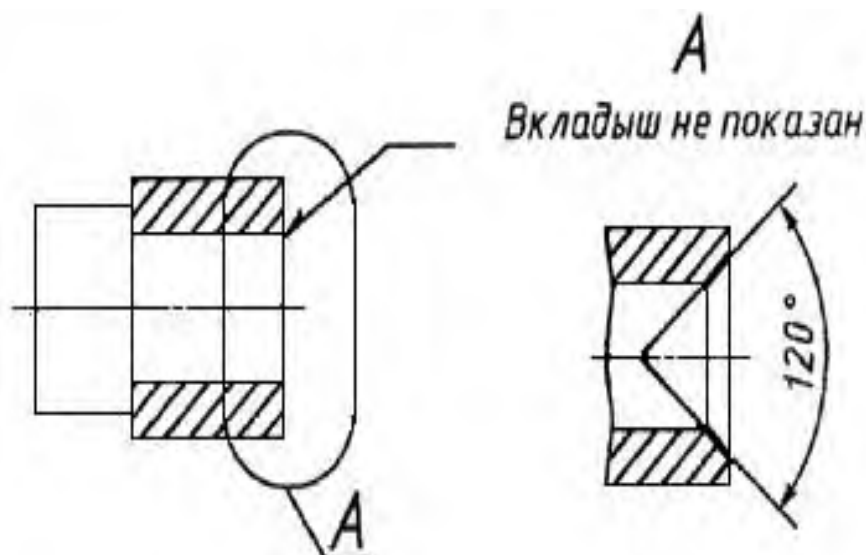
Пример изображения участка изделия, подлежащего ремонту, для изделий, ремонтируемых сваркой, пайкой, нанесением металлопокрытия и т.п.
